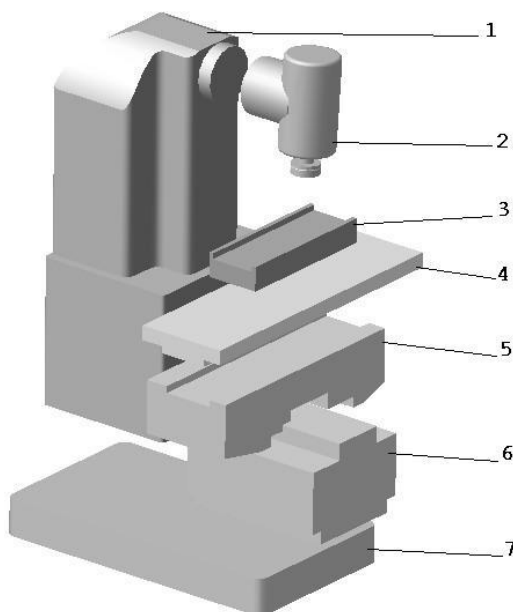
Элементы расчетной схемы упругой системы плоско-шлифовального станка
